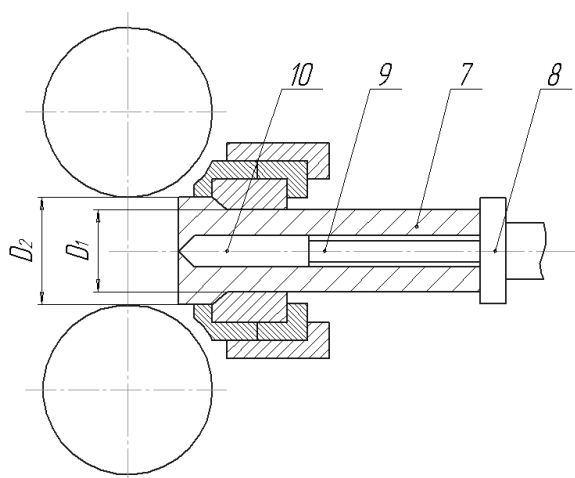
Схема устройства на стадии прошивки и процесса прессования: 7 – прессуемый полый профиль; 8 – пресс-шайба; 9 – пуансон; 10 – пресс-игла
